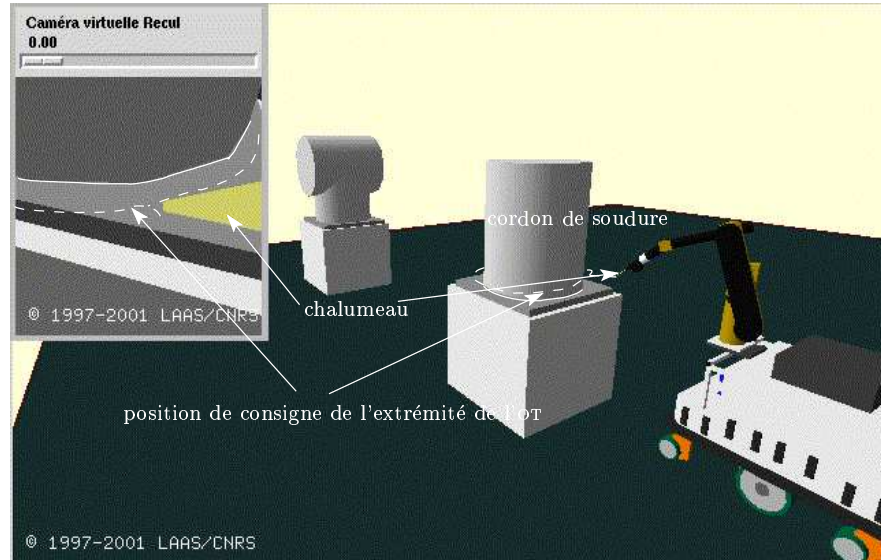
Mouvement opérationnel pour souder deux pièces
